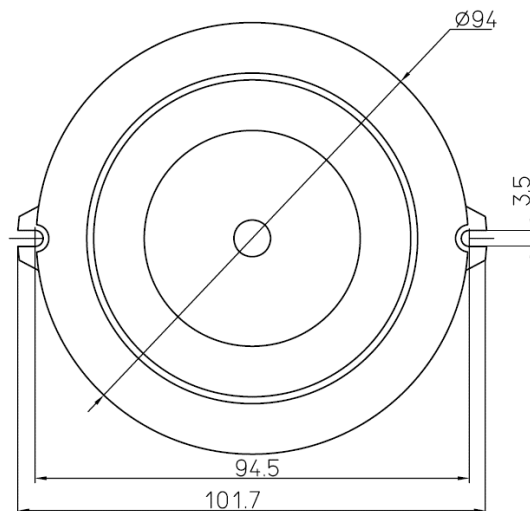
Габаритные и присоединительные размеры корпуса ОСЗ
